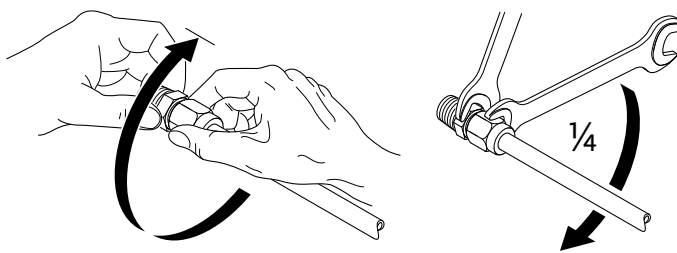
Дополнительный поворот резьбового соединения с обжимным кольцом на 1/4 оборота
